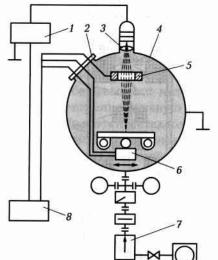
Установка для сварки электронным лучом:
